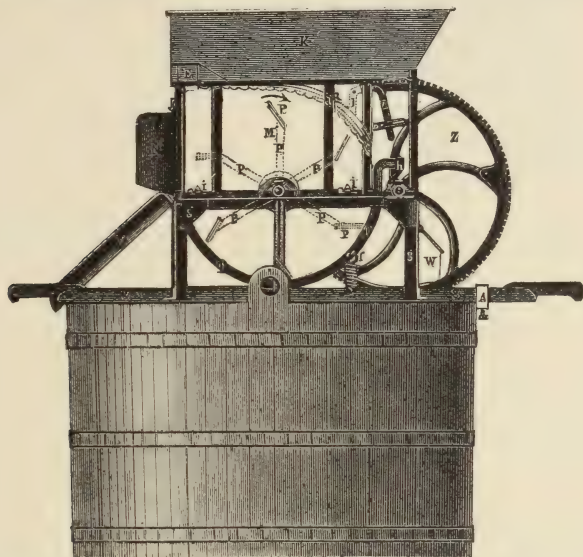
Abbeer- und Quetschmaschine „Brüggemann“ (Innenansicht)
